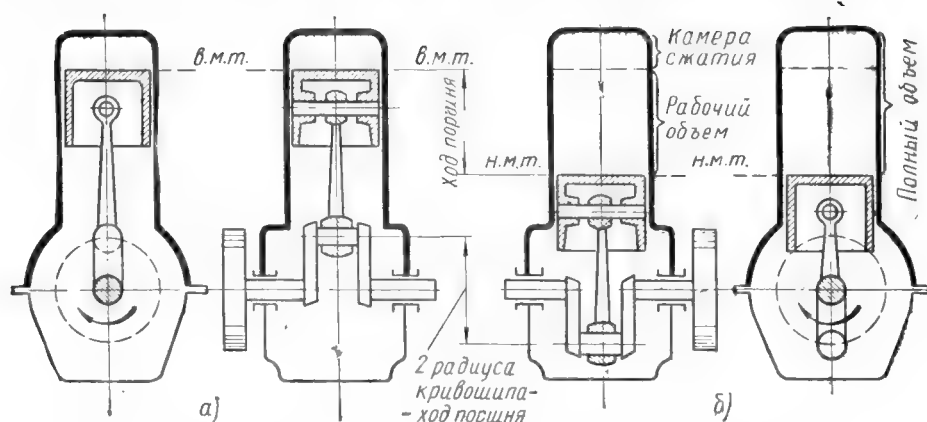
Кривошипно-шатунный механизм двигателя внутреннего сгорания.
